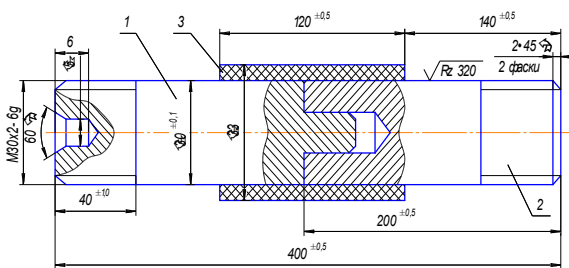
Конструктивні розміри збірної зразка для досліджень склеєних з'єднань: 1, 2 – ліва і права оправки; 3 – намотаний шар із АПМ
